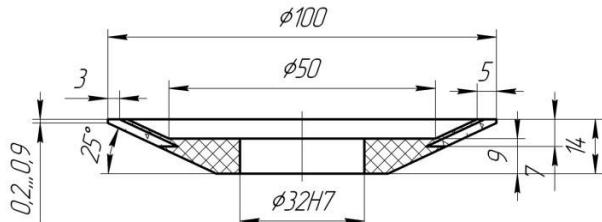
Чертёж круга формы 12R4 100×3×7 с корпусом из композита
